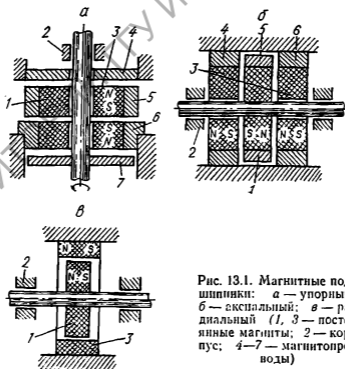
Магнитные подшипники: а — упорный; б — аксиальный; в — радиальный (1, 3 — постоянные магниты; 2 — корпус; 4—7 — магнитопроводы)
